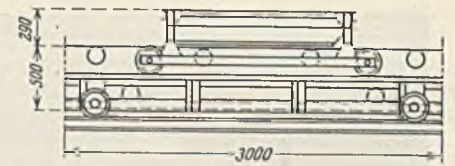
Ausschnitt aus dem beweglichen Bande mit fahrbarer Aufnahmeschurre.
